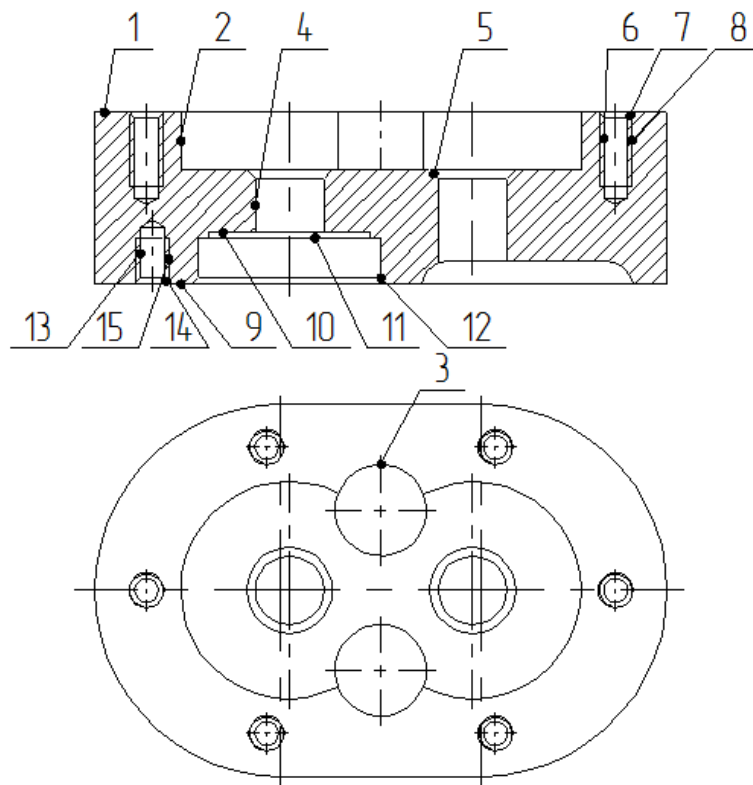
Послідовність оброблення поверхонь деталі «Корпус шестерного насоса»
